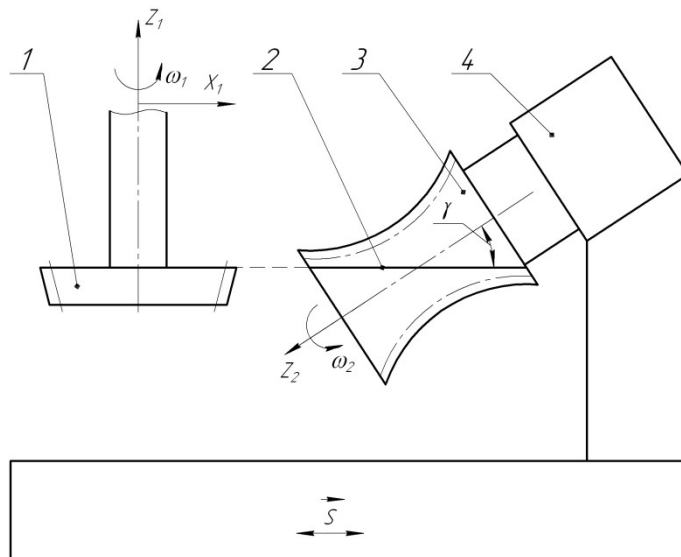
Схема формообразования витков шлифовального круга на поверхности однополостный гиперboloид долбяком: 1 –долбяк; 2 – прямолинейная образующая винтовой гиперboloидной поверхности; 3 – гиперboloидная заготовка шлифовального круга; 4 – делительная головка
